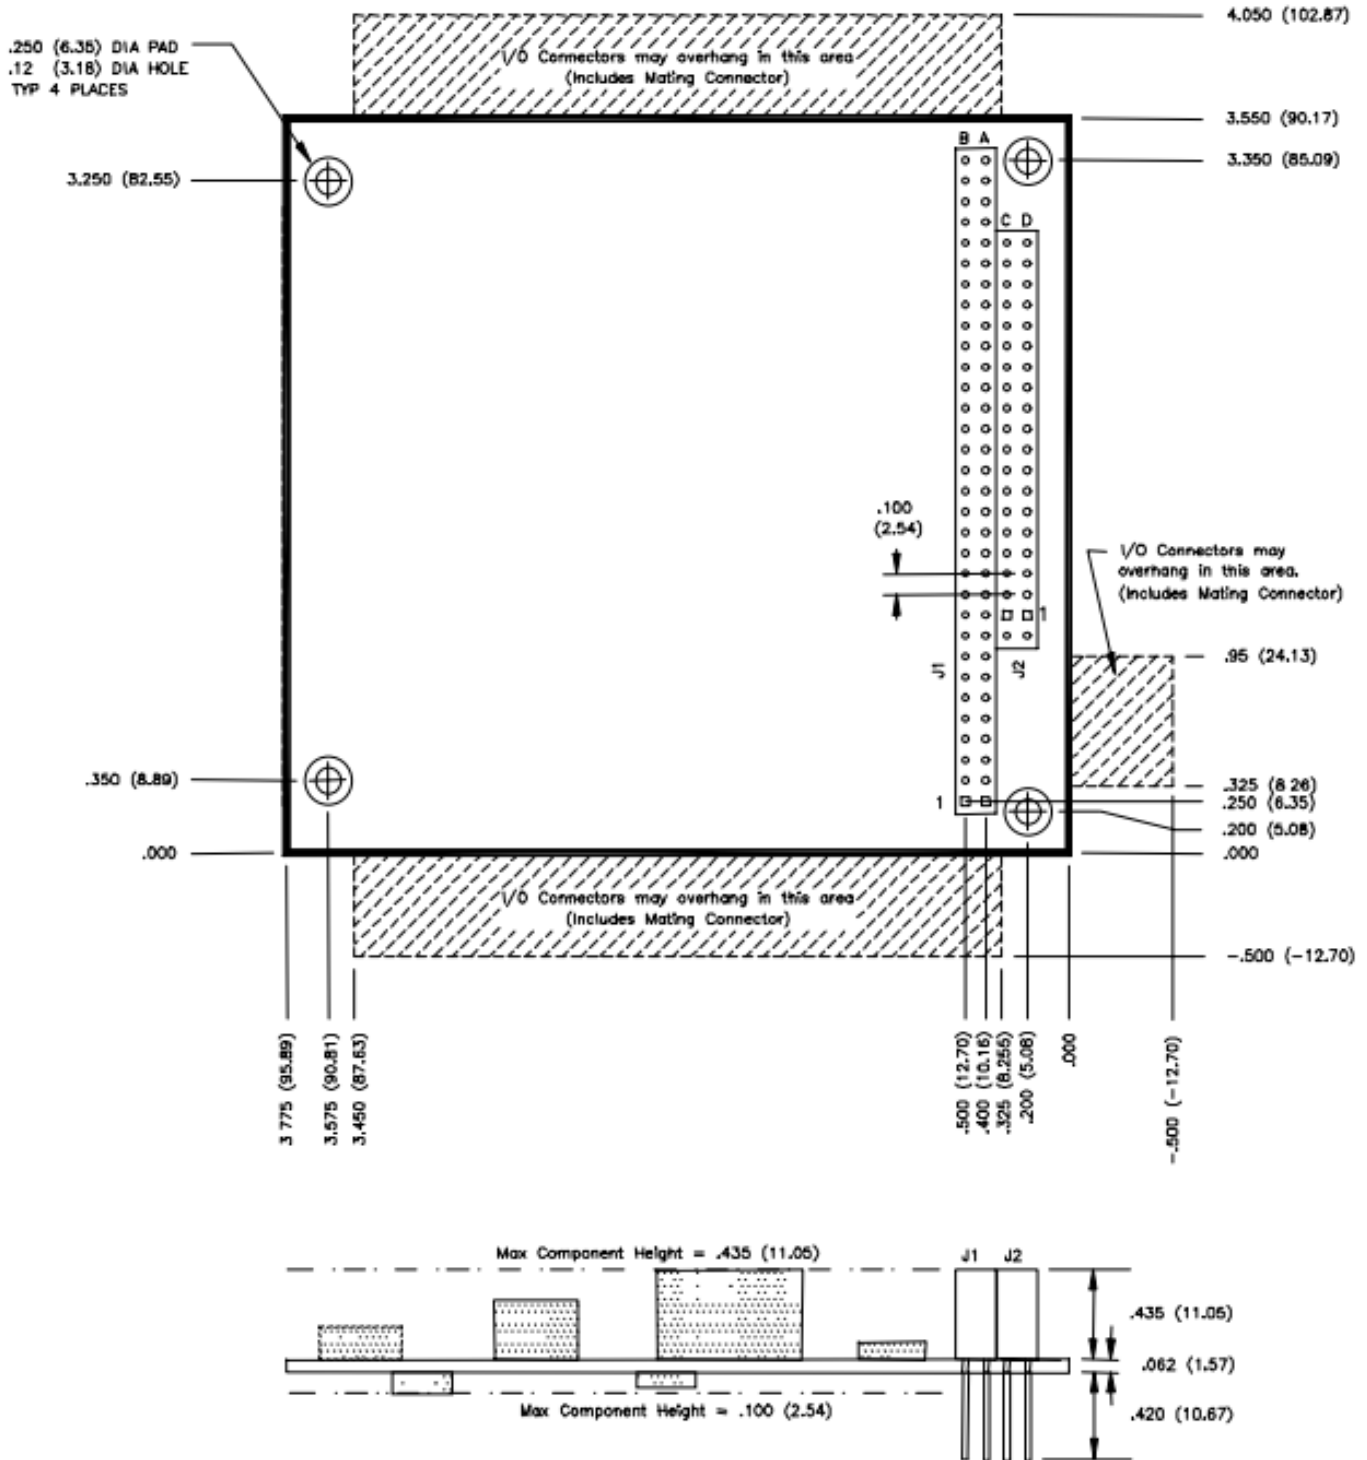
Dimensiones de PCB de acuerdo con estándar PC/104
